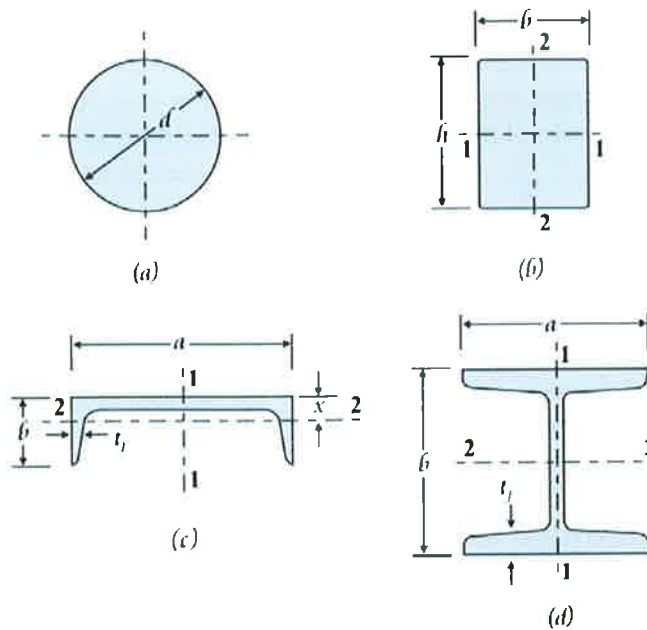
Perfiles estructurales, a) barra redonda maciza; b) barra de sección rectangular; c) canal; d) viga I de patín ancho.
